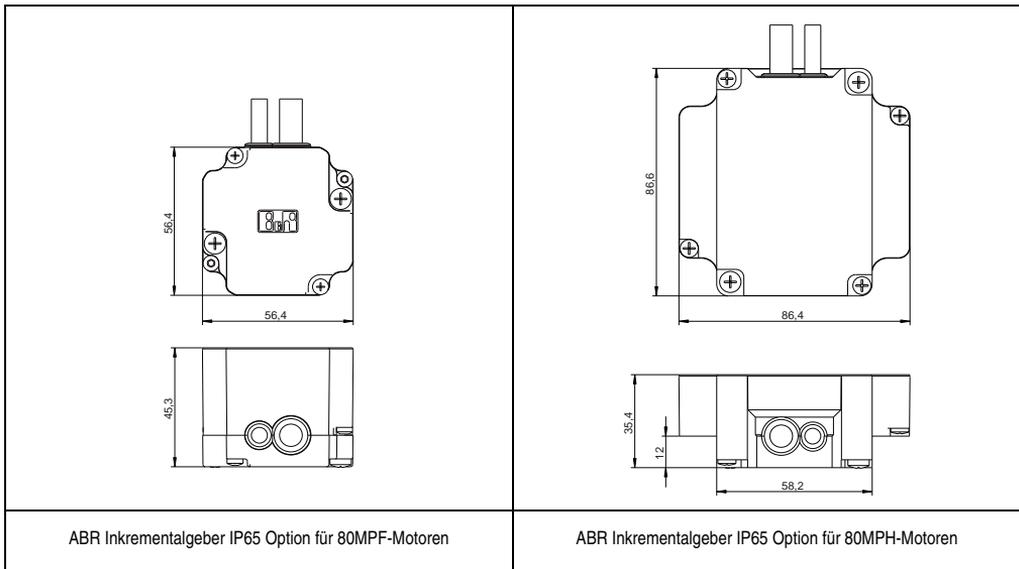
Schrittmotoren mit ABR Inkrementalgeber IP65 Option - Abmessungen
